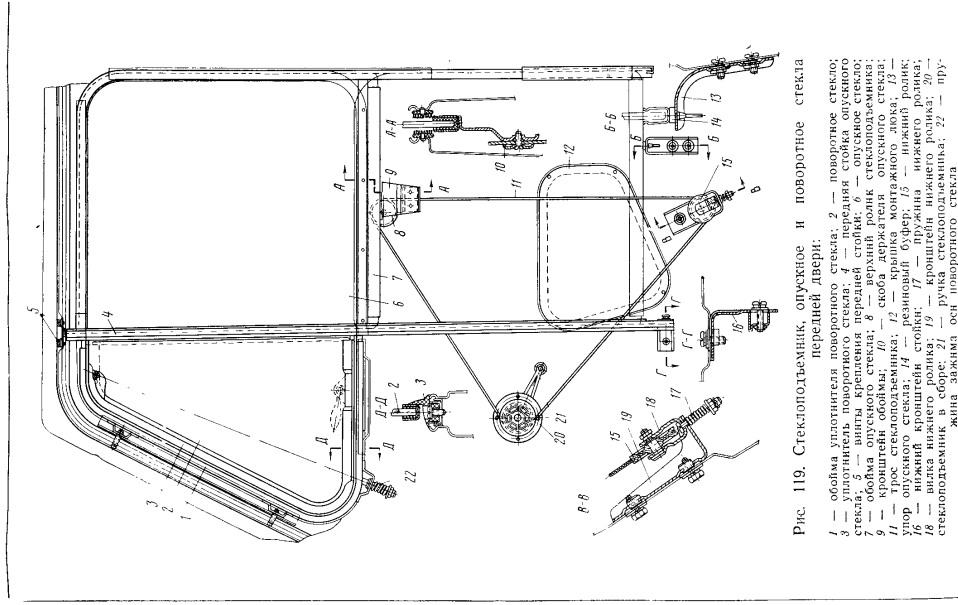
Стеклоподъемник, опускающий и поворачивающий переднюю дверь:
